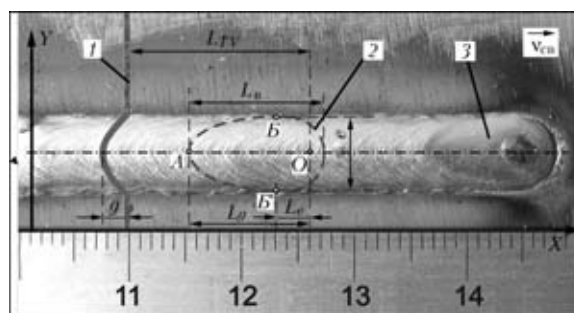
Схема возникновения транспортных запаздываний между сварочной ванной и ЛТС при сварке МАГ: 1 — световой след ЛТС; 2 — воображаемый контур сварочной ванны; 3 — поверхность затвердевшей сварочной ванны
